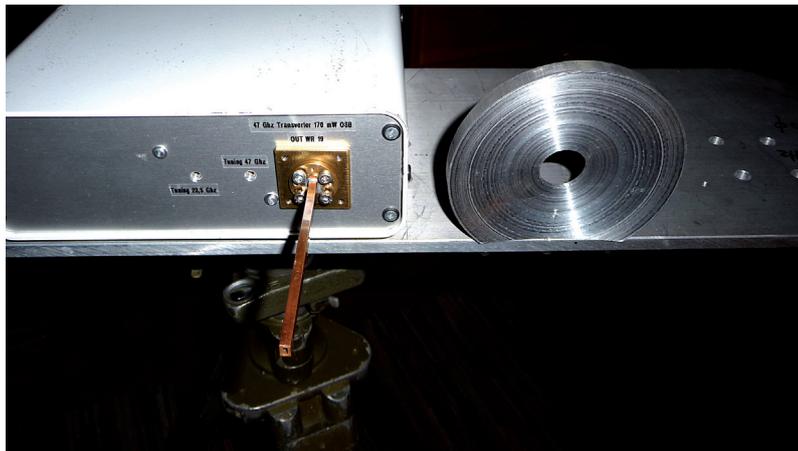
Bearbeitete Aluscheibe auf Parabol aufgelegt
